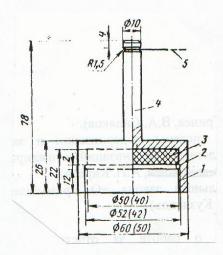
Магнитная головка для натяжения струны при измерении перехода рычагов через «мертвую точку»: 1 - корпус; 2 - сухарь; 3 - магнитный вкладыш; 4 - стержень; 5 - струна.
